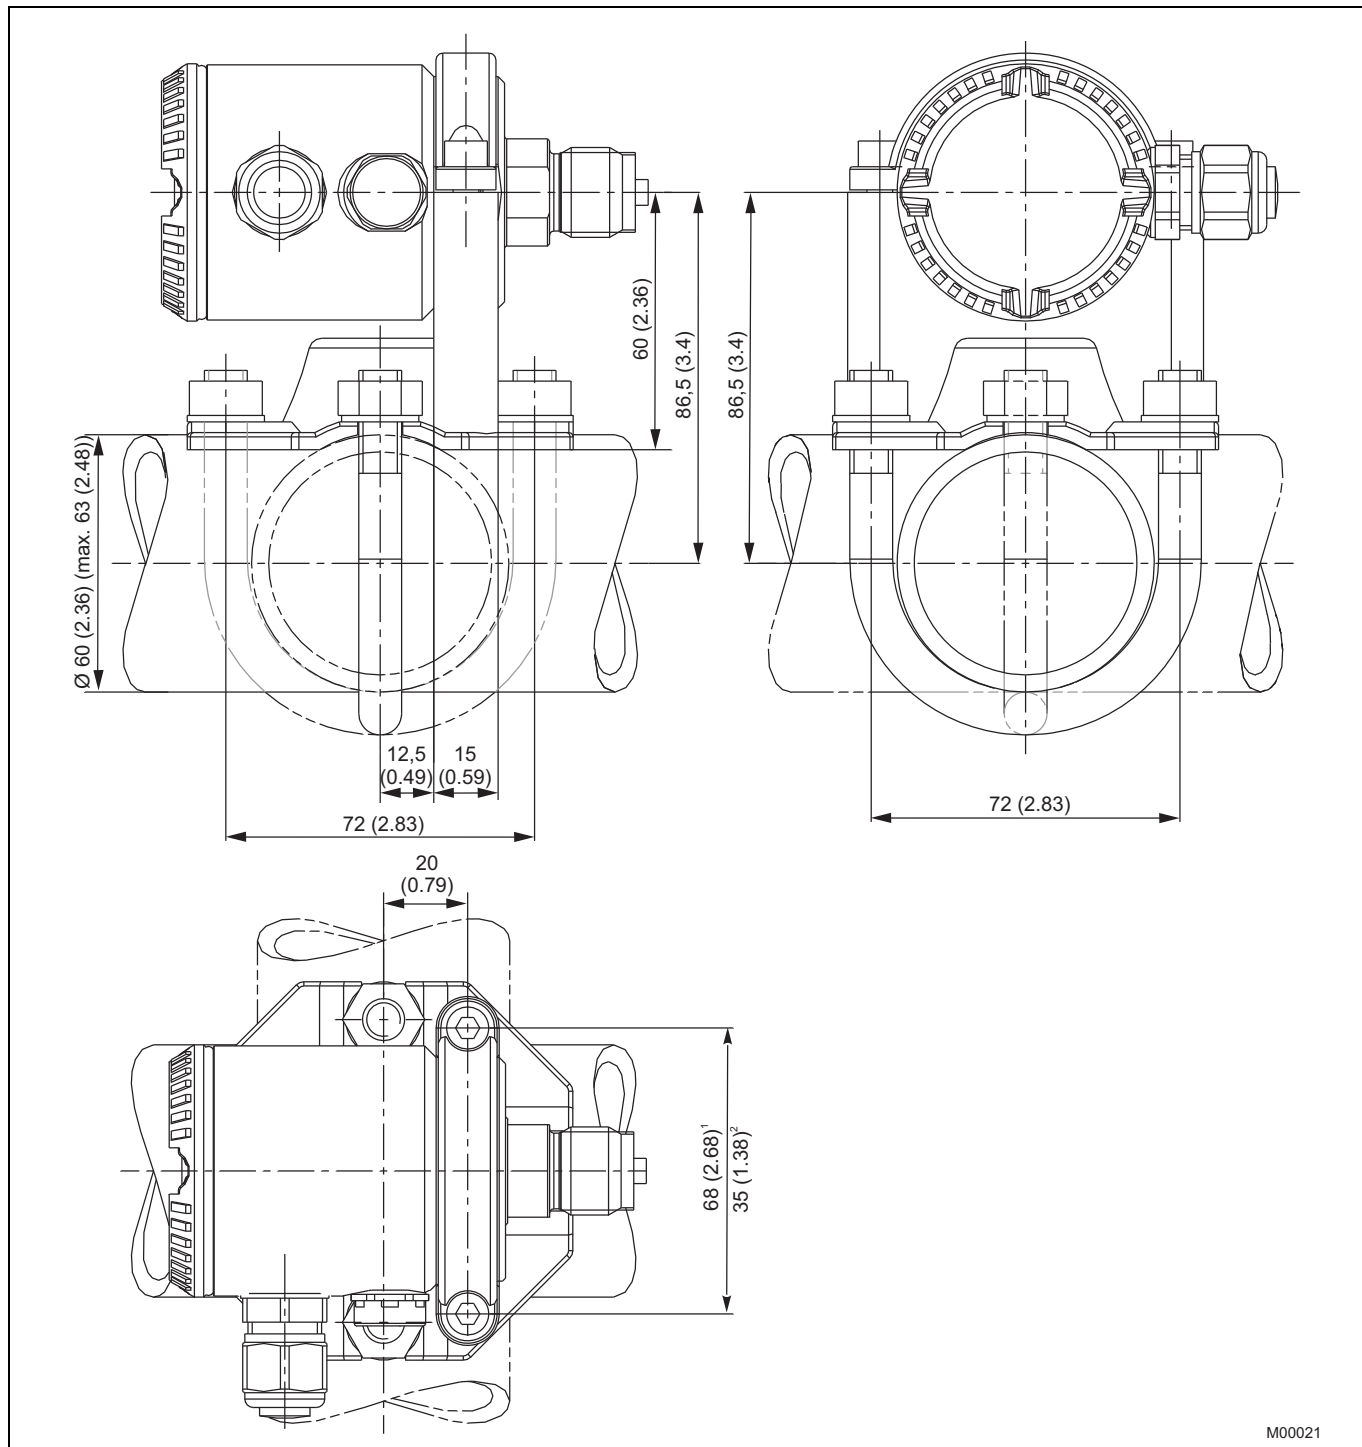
Настенный монтаж / монтаж на трубе (размеры указаны в мм (дюймах))
